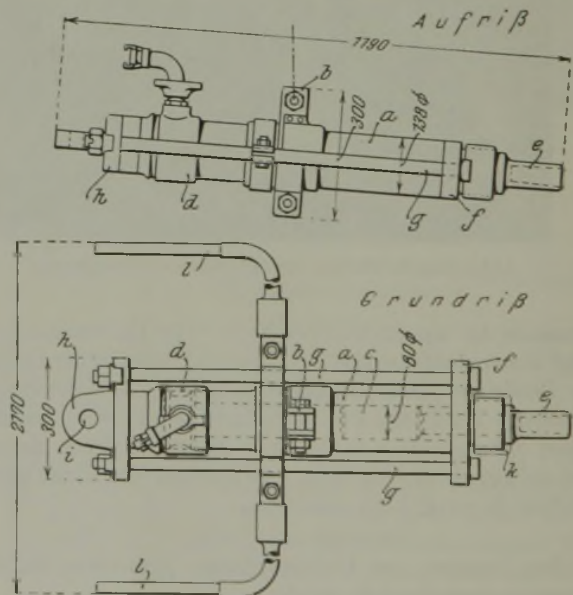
Aufriß und Grundriß des Stichlochhammers.
